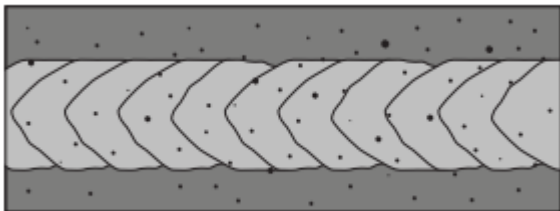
Défaut de projection (ou de collage) dans un joint soudé (Réf.[R16])
